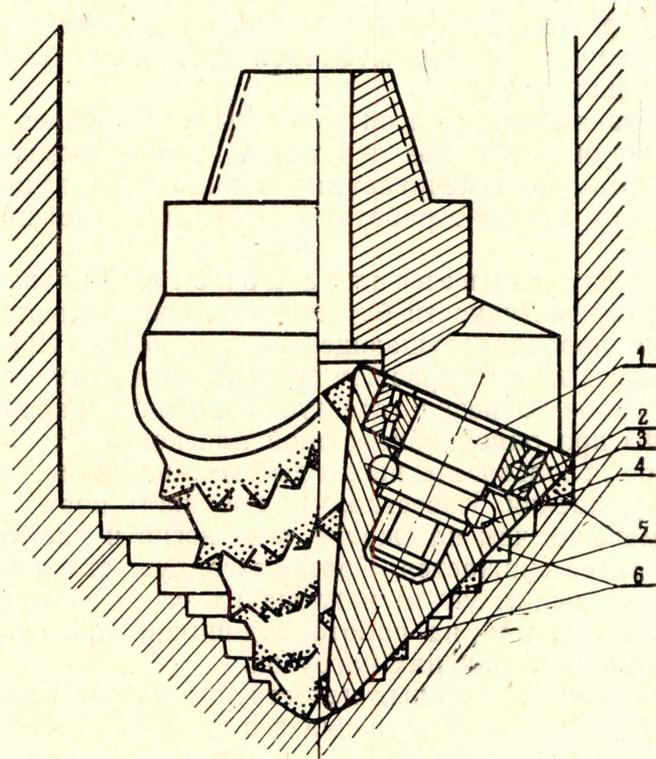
Шарошечное ступенчатое долото: 1 — цапфа; 2 — шарошка; 3 — радиально-упорный подшипник; 4 — шариковый замковый подшипник; 5 — зубья шарошек; 6 — ступени забоя
